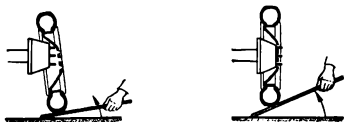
Ausnutzen des Hebels beim Aufsetzen schwerer Räder
